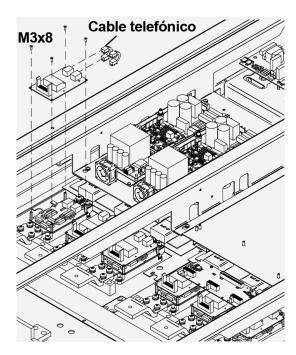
Extracción Tarjeta Gate-Drive superior
